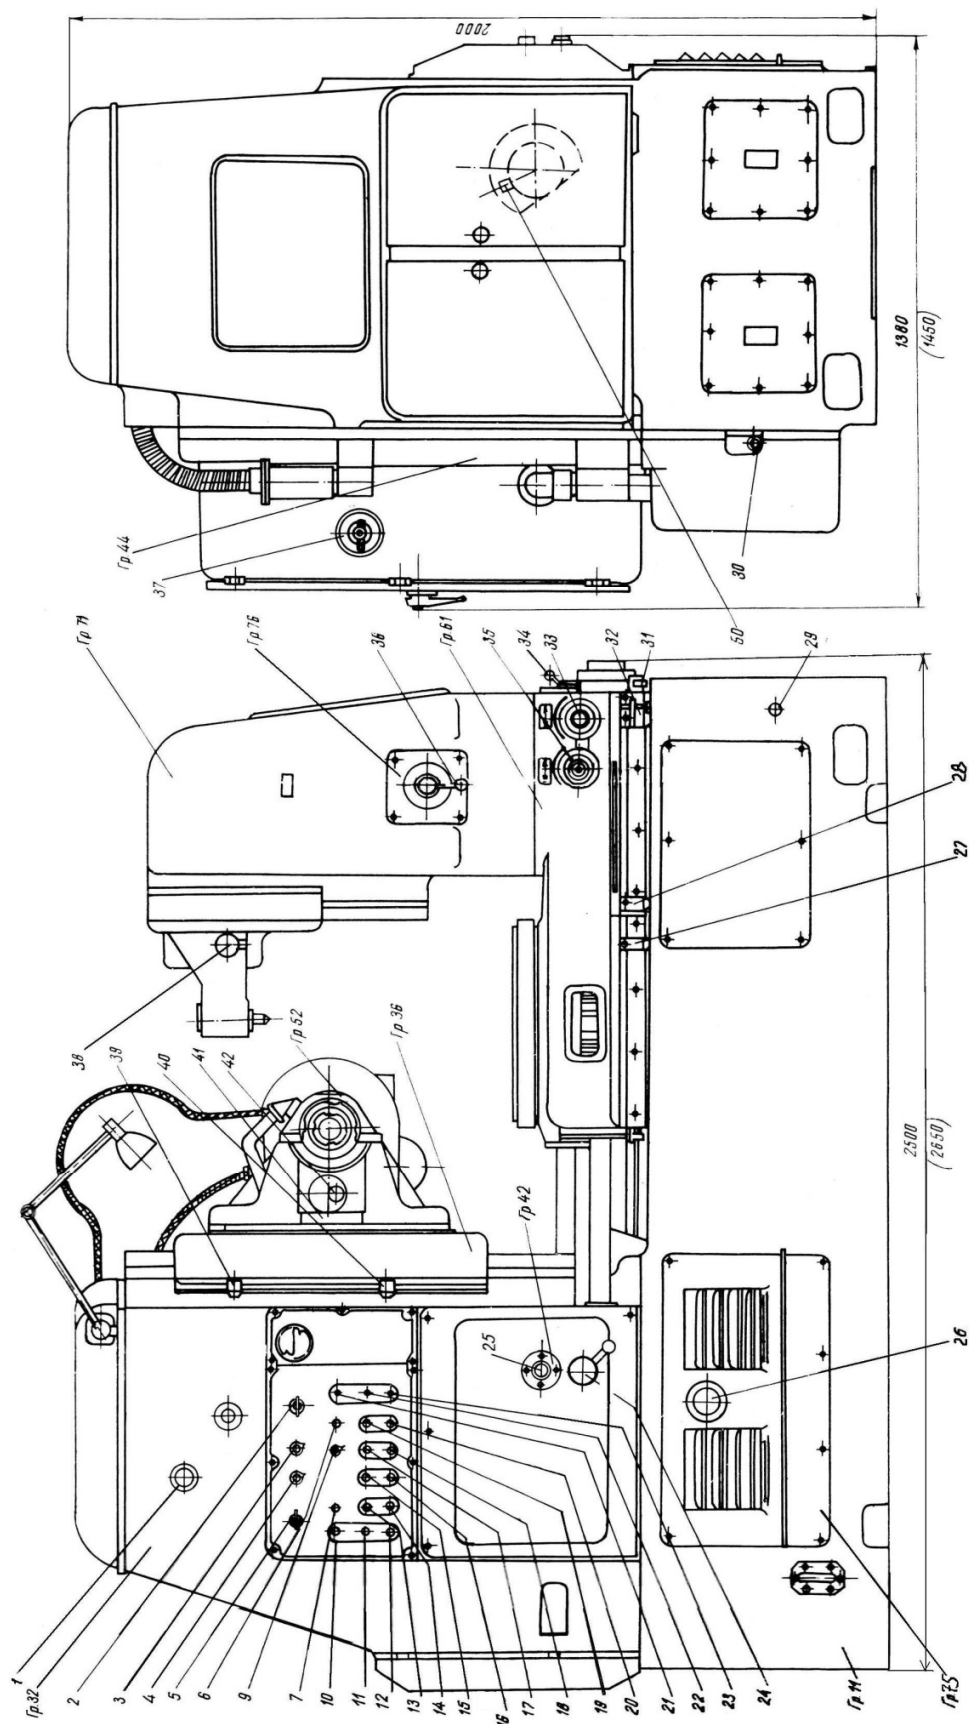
Общий вид зубофрезерного станка 5K32A
